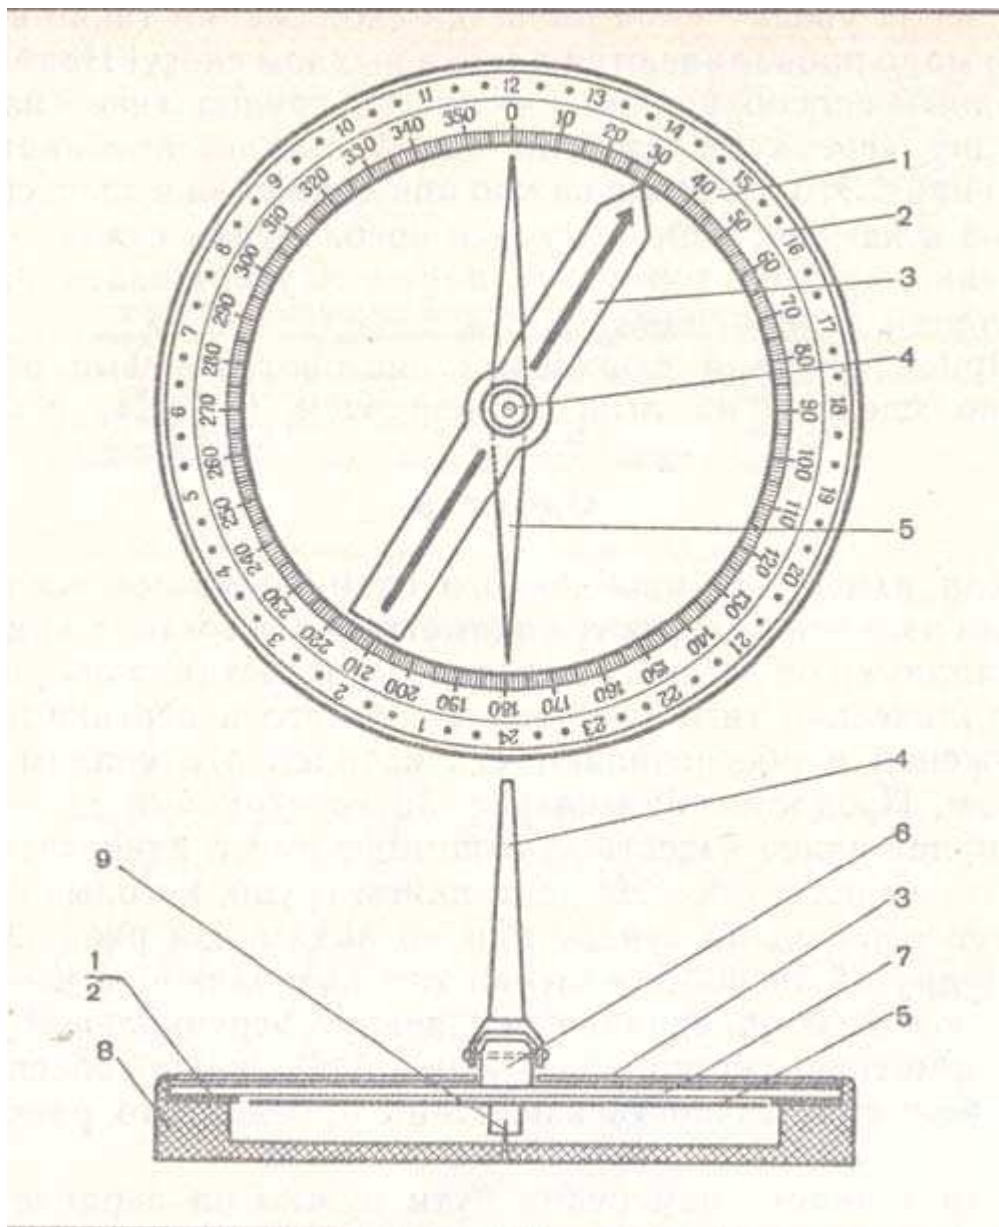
Солнечно-магнитный компас: 1 — лимб компаса; 2 — часовой лимб; 3 — визир; 4 — откидная стойка; 5 — магнитная стрелка; 6 — ось откидной стойки; 7 — прозрачная крышка; 8 — корпус компаса; 9 — ось магнитной стрелки.
